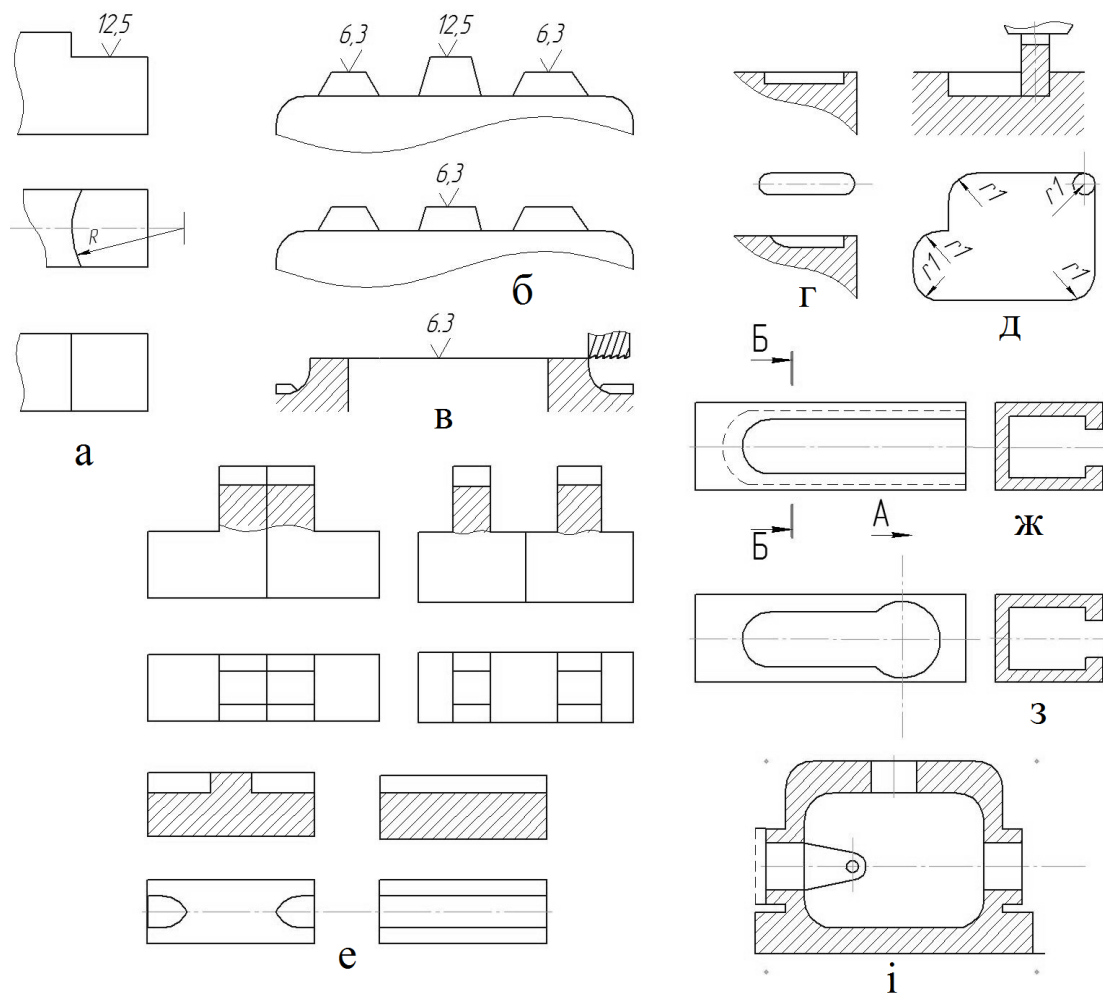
Приклади поліпшення технологічності деталей, оброблюваних на фрезерних верстатах
